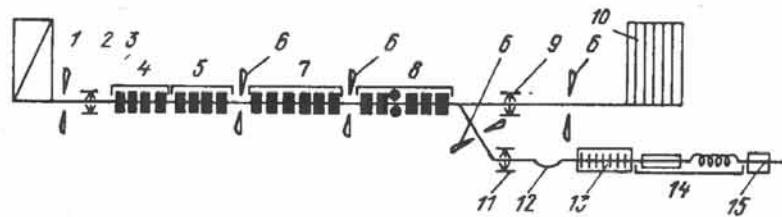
Схема расположения оборудования мелкосортно-проводочного стана 320/150:
